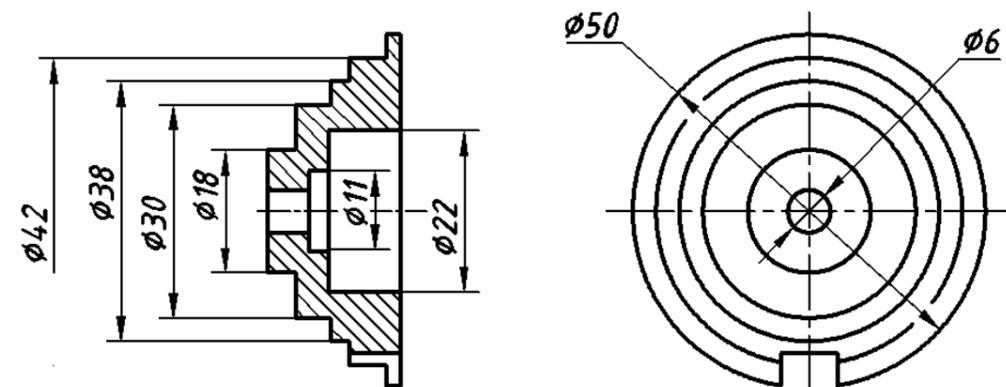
Предпочтительное нанесение размеров поверхностей вращения
